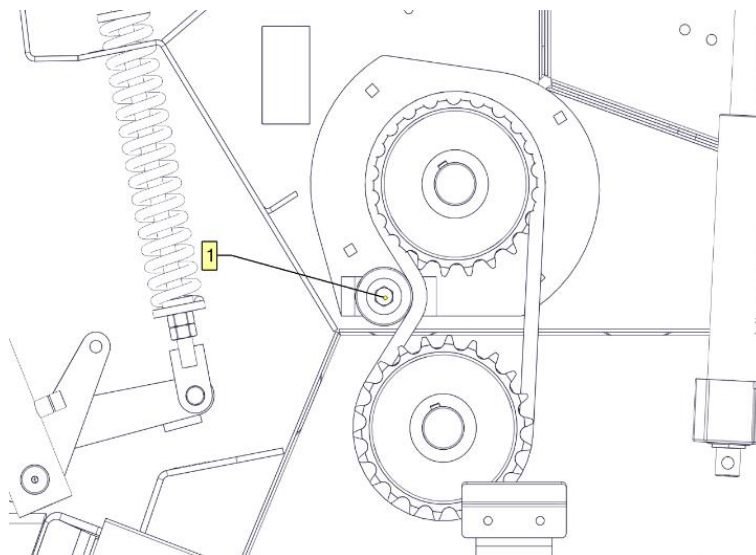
Регулировка натяжения цепи с правой стороны пресс-подборщика
